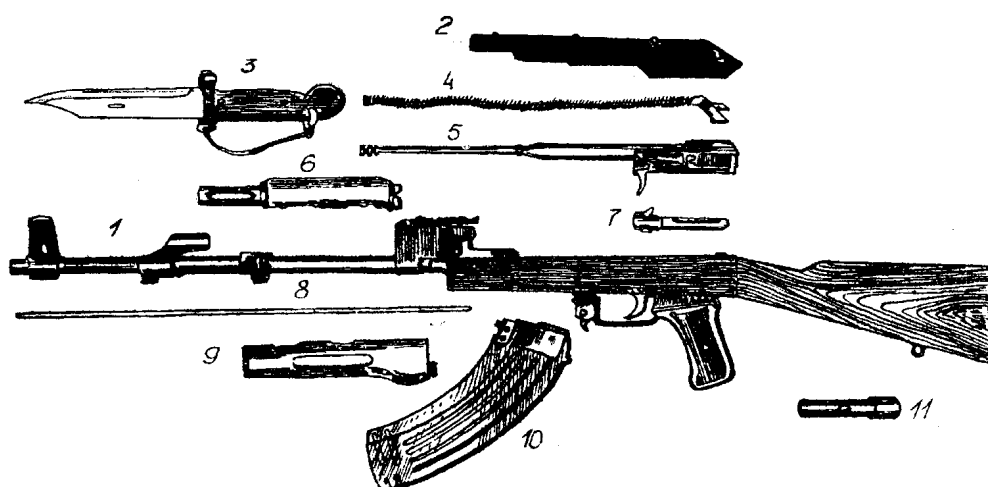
Основні частини та механізми автомата: 1 - ствол зі ствольною коробкою; 2 - кришка ствольної коробки; 3 - багнет-ніж; 4 - поворотальний механізм; 5 - затворна рама з газовим поршнем; 6 - газова трубка зі ствольною накладкою; 7 - затвор; 8 - шомпол; 9 - цев'є; 10 - магазин; 11 - пенал з приладдям
